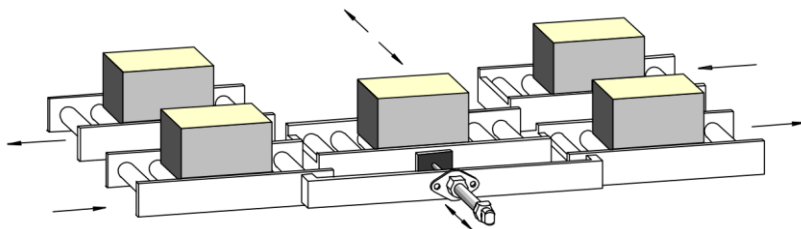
Схема переміщення деталей між конвеєрними стрічками
